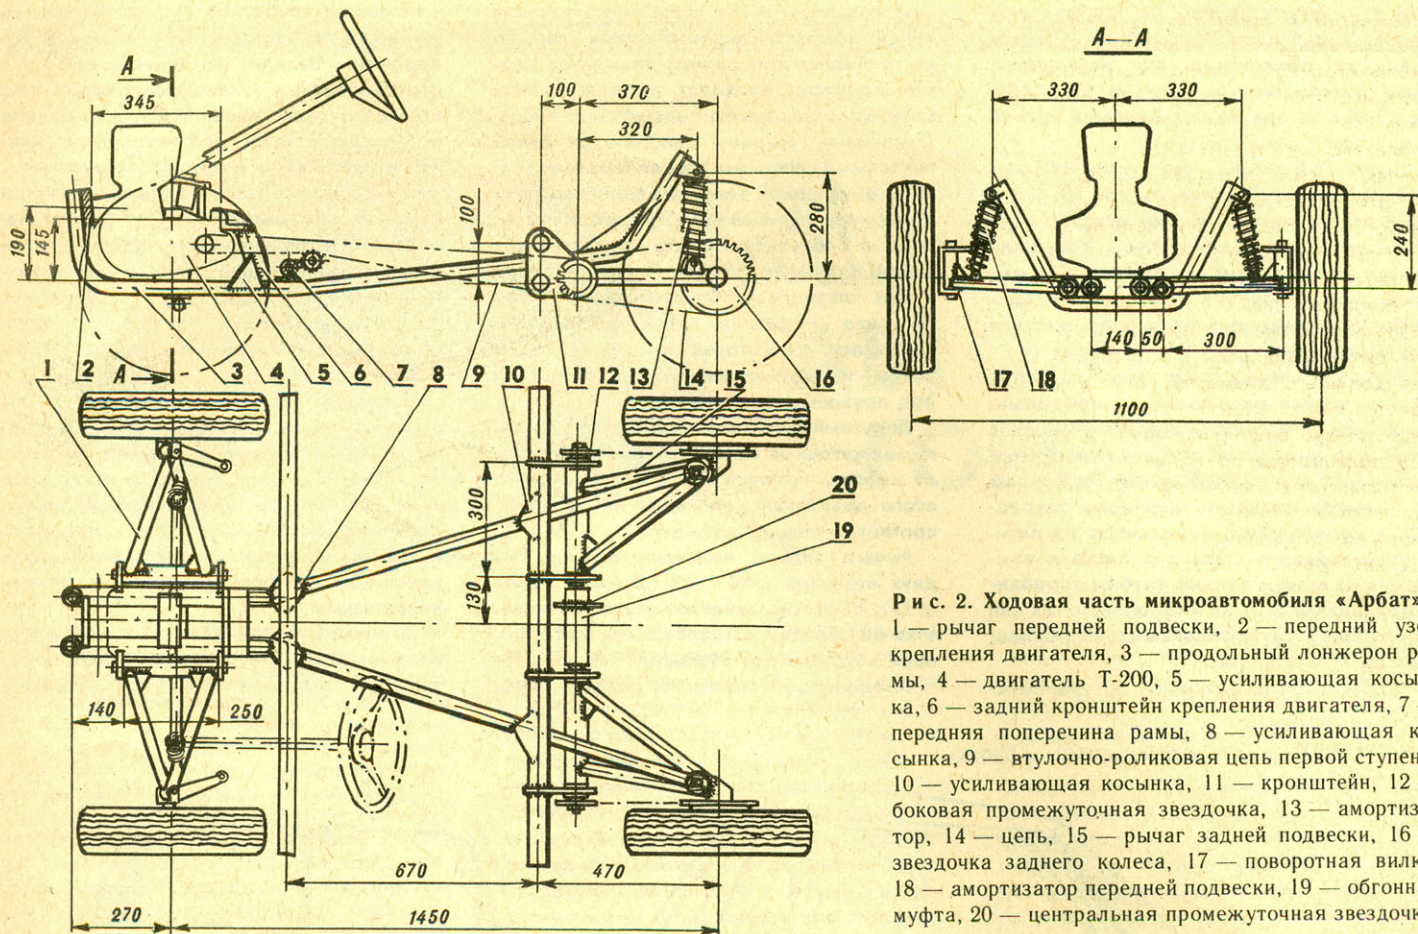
Ходовая часть микроавтомобиля «Арбат»: 1 — рычаг передней подвески, 2 — передний узел крепления двигателя, 3 — продольный лонжерон рамы, 4 — двигатель Т-200, 5 — усиливающая косынка, 6 — задний кронштейн крепления двигателя, 7 — передняя поперечина рамы, 8 — усиливающая косынка, 9 — втулочно-роликовая цепь первой ступени, 10 — усиливающая косынка, 11 — кронштейн, 12 — боковая промежуточная звездочка, 13 — амортизатор, 14 — цепь, 15 — рычаг задней подвески, 16 — звездочка заднего колеса, 17 — поворотная вилка, 18 — амортизатор передней подвески, 19 — обгонная муфта, 20 — центральная промежуточная звездочка.
